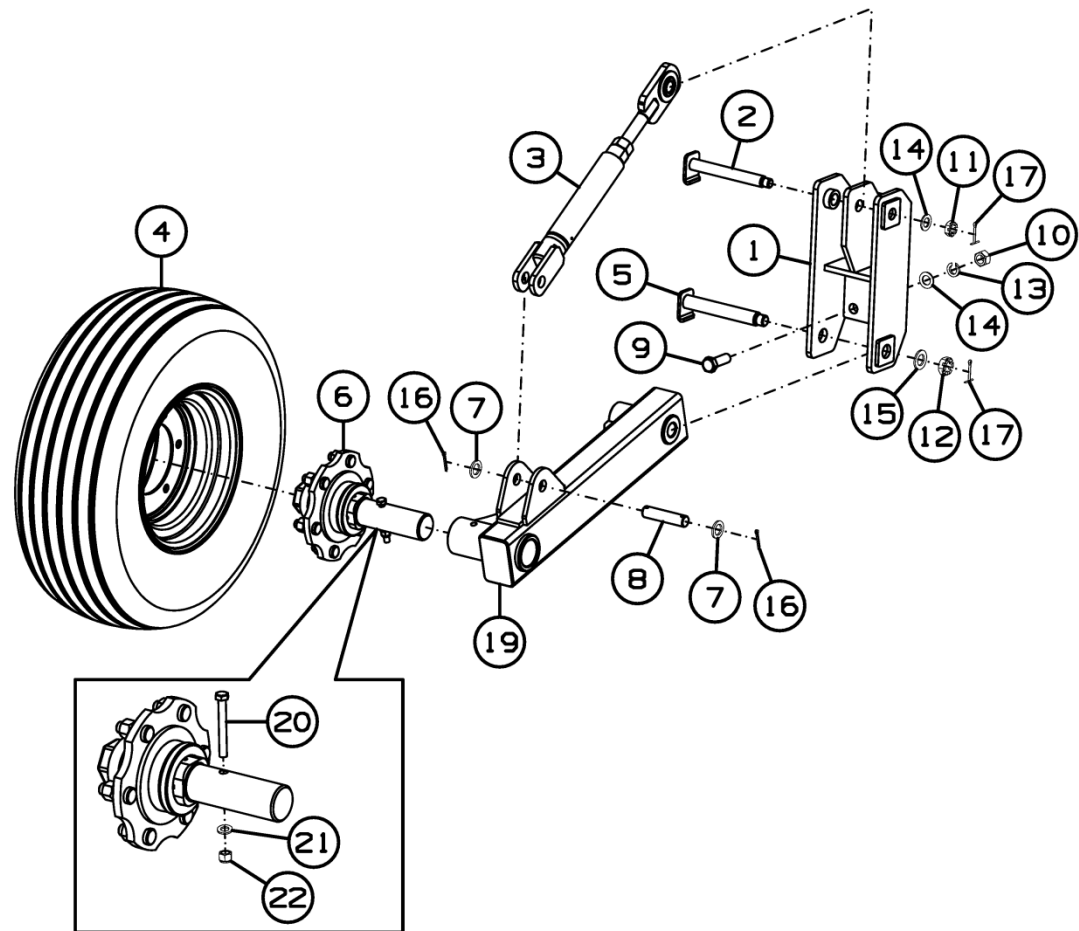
Колесо опорное СГ-122.06.000 и СГ-122.06.000-01
